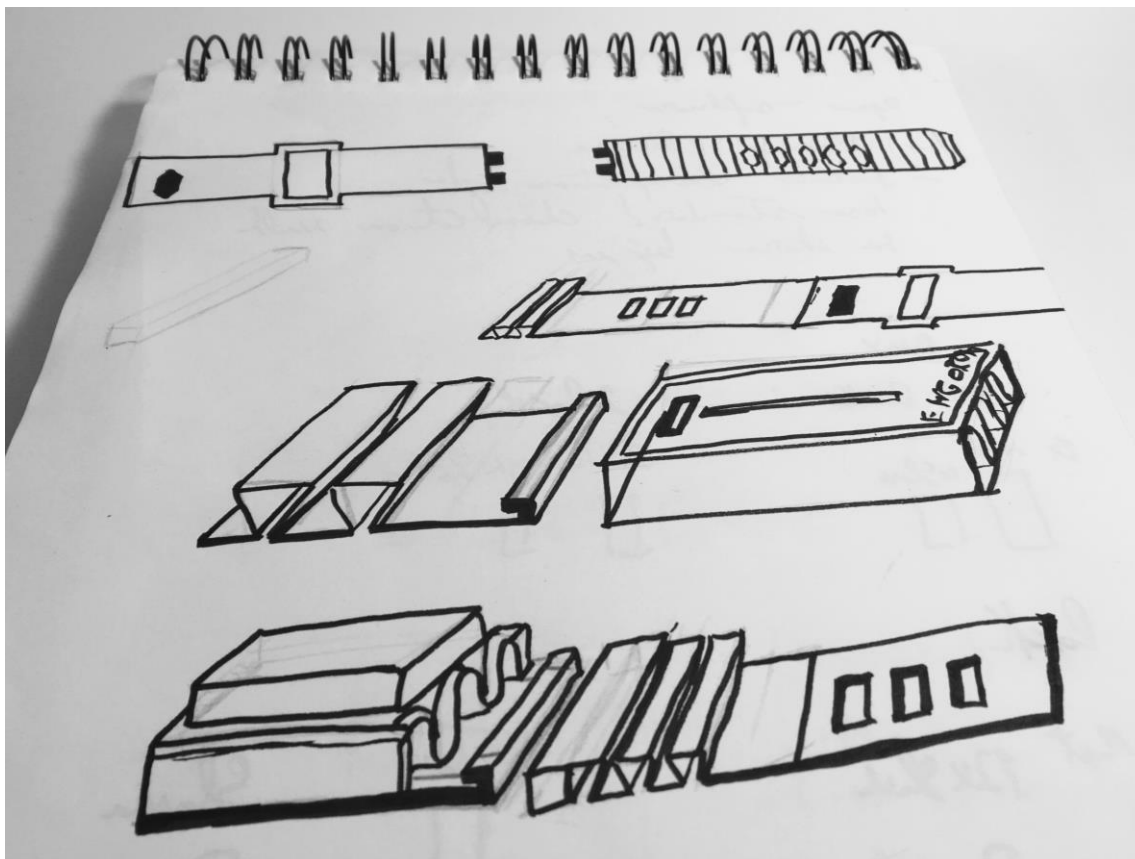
Esboço do Módulo Principal e Sistemas de Encaixe com Mola.
